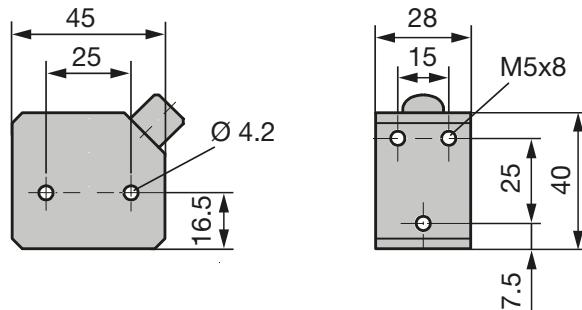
Einbaumaße Positionsgeber BTL5-P-4500-1
